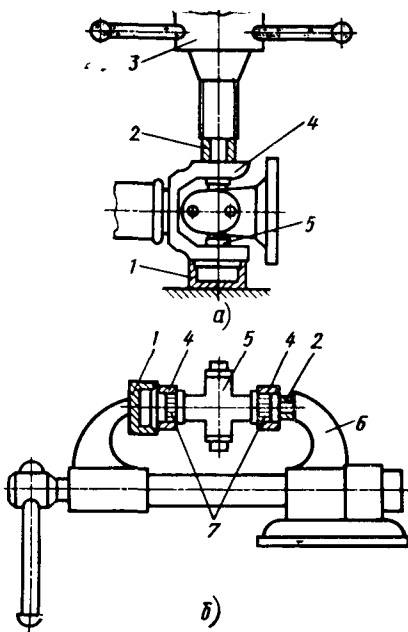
Приспособления для выпрессовки подшипников крестовин карданных валов:
